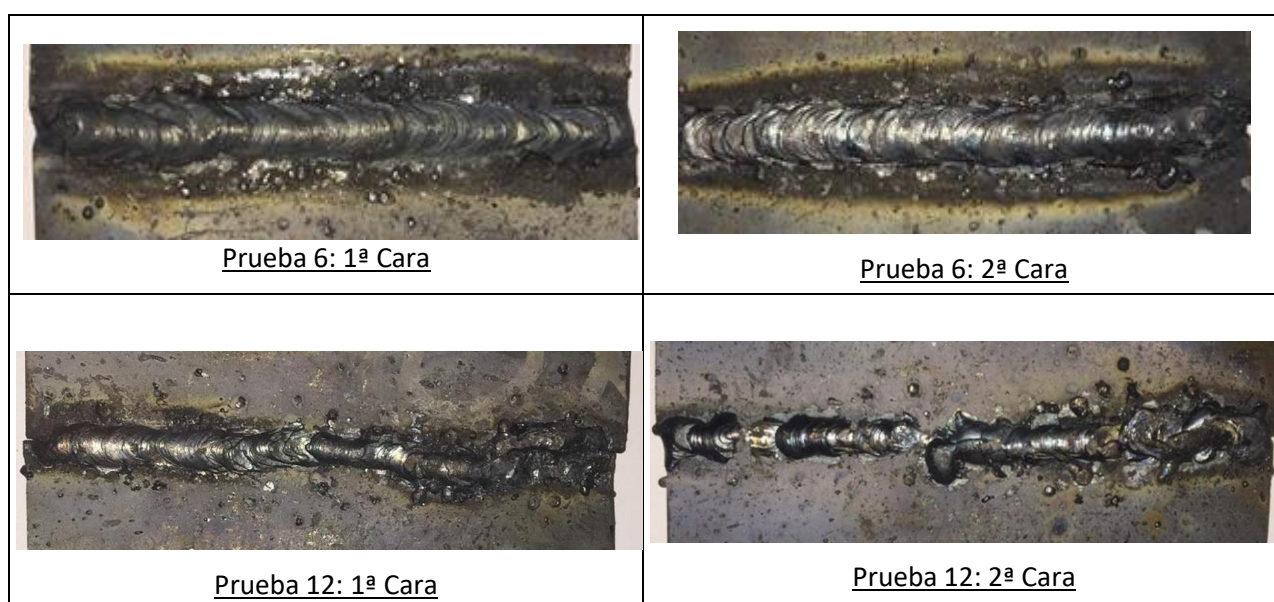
Fotografías de los cordones de soldadura por ambas caras de las pruebas 6 y 12. Fuente: Propia.
